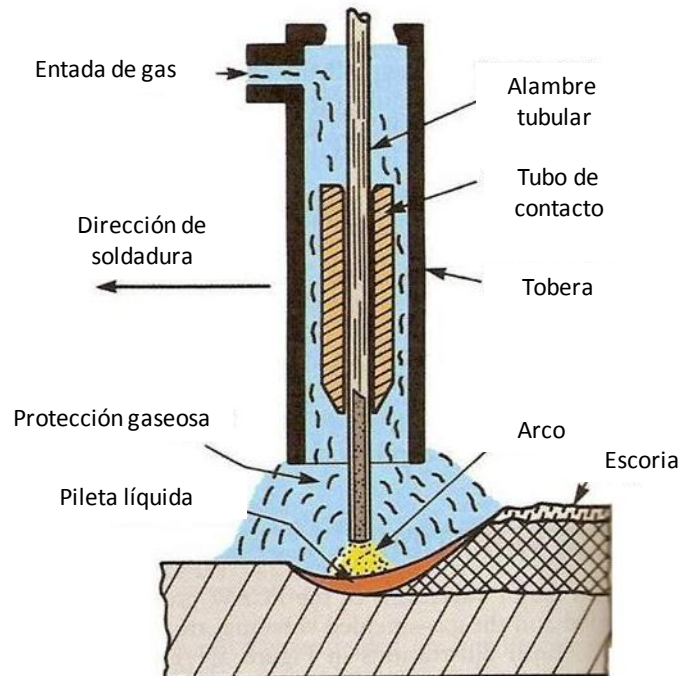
12. Proceso de soldadura con electrodo tubular y protección gaseosa.
